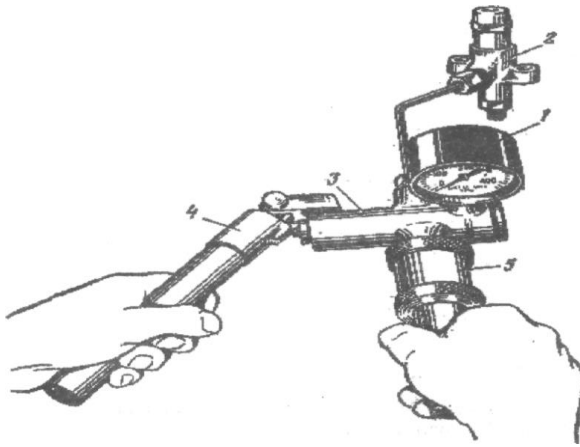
Пристрій КИ- 9917 для перевірки форсунок: 1 – манометр; 2– форсунка, що випробовується; 3 – корпус; 4 – важіль; 5 – резервуар для палива
